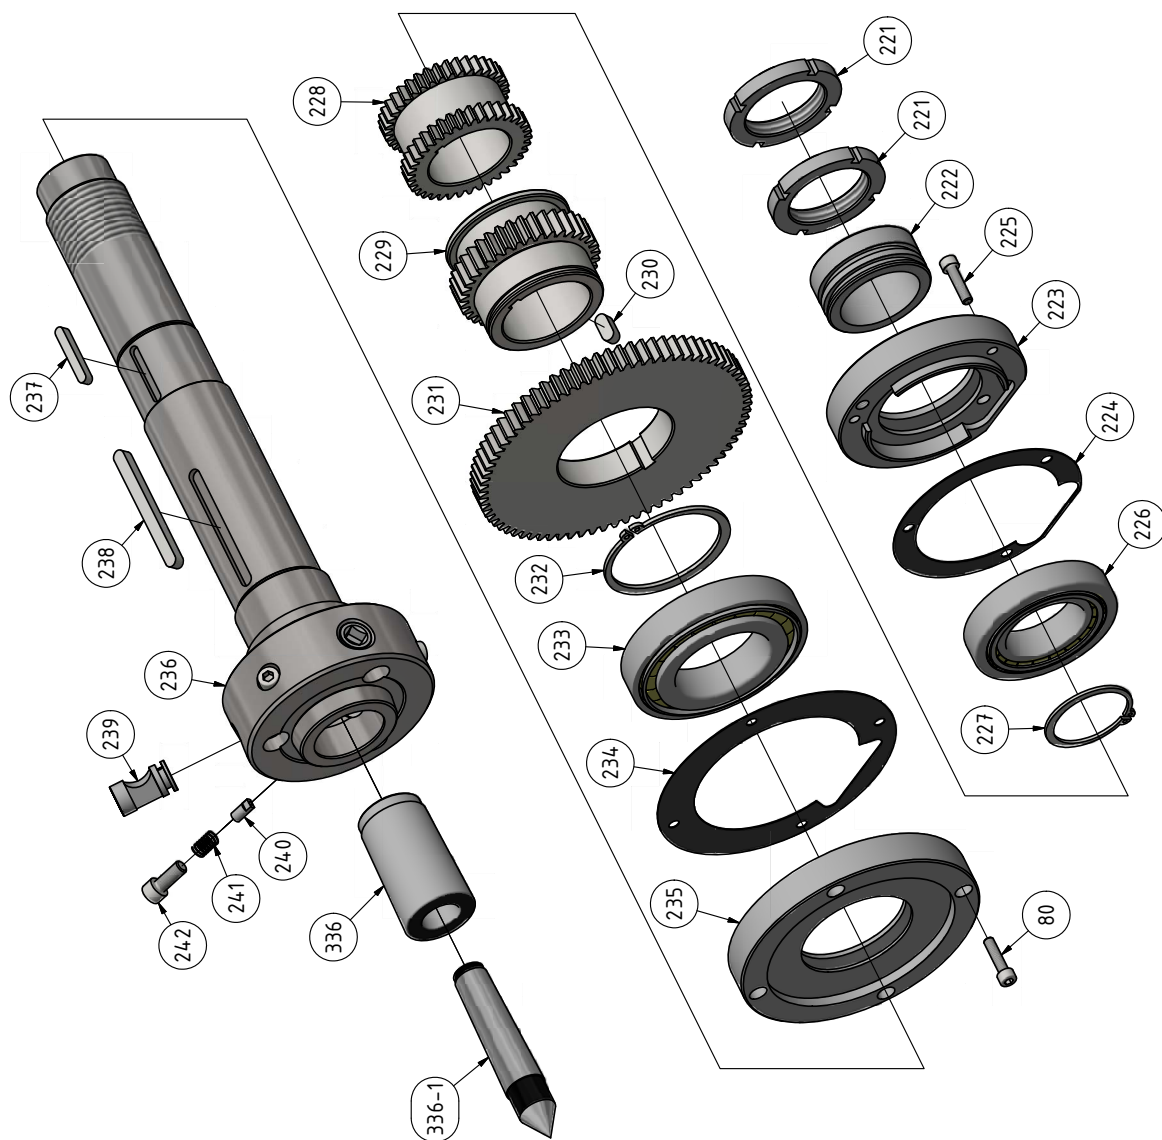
Getriebe Spindelstock 3-6 - Headstock gear 3-6
